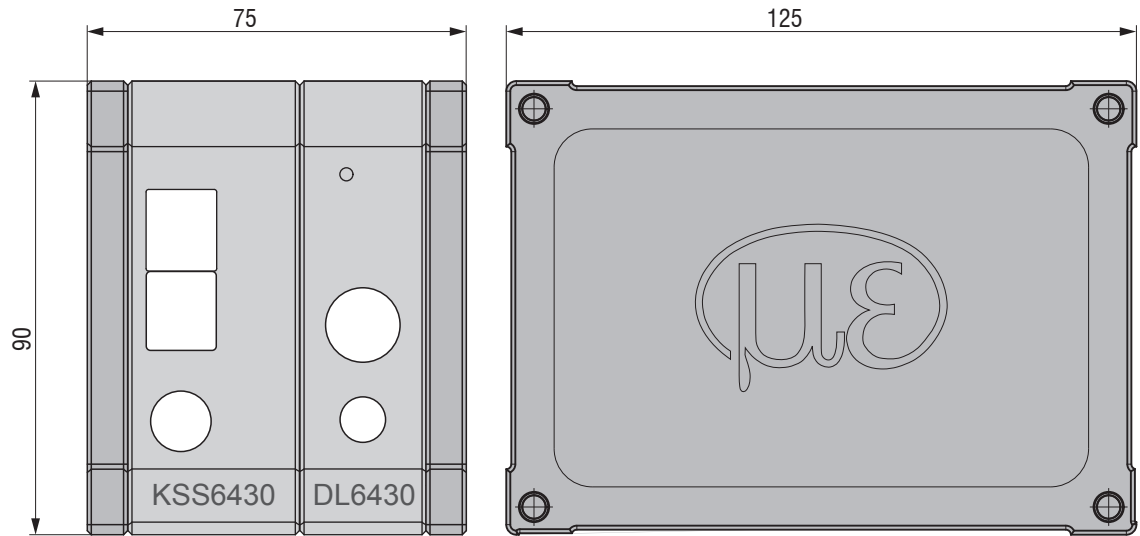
Maßzeichnung Controller mit Basiseinheit, Demodulator und Gehäusedeckel
